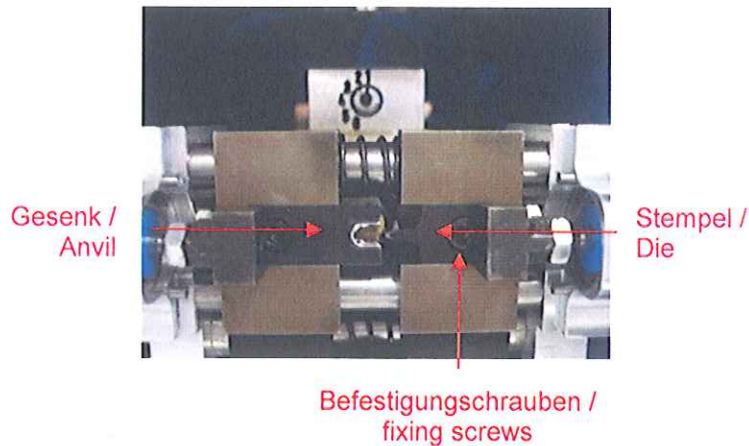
Crimpwerkzeug / Crimping tool
